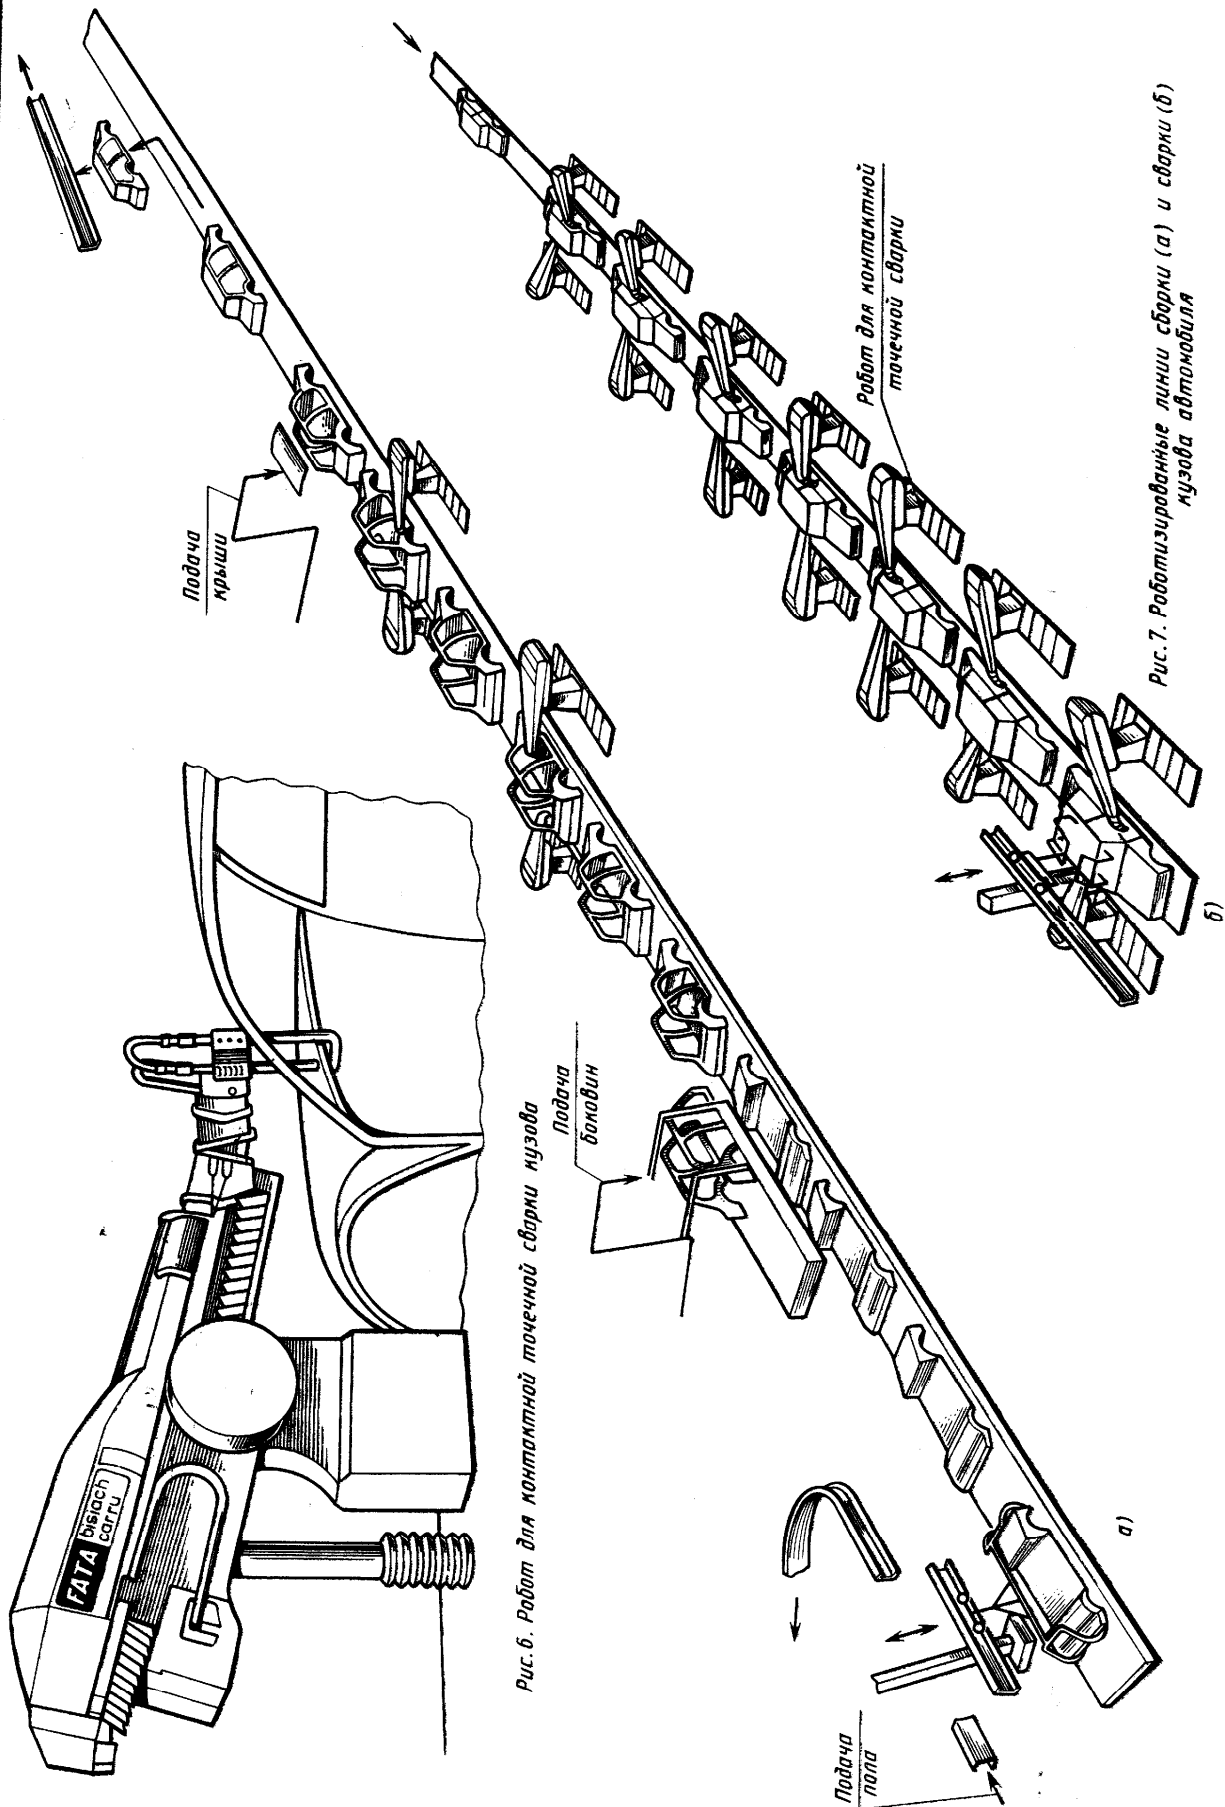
Робот для контактной точечной сварки кузова
